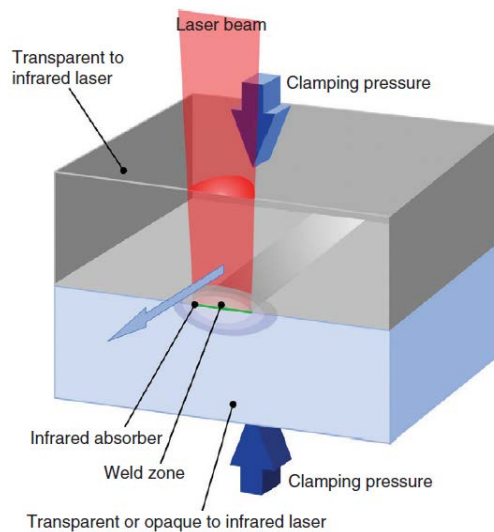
Esquema del proceso de soldadura láser por transmisión (Fuente: TWI Ltd).
